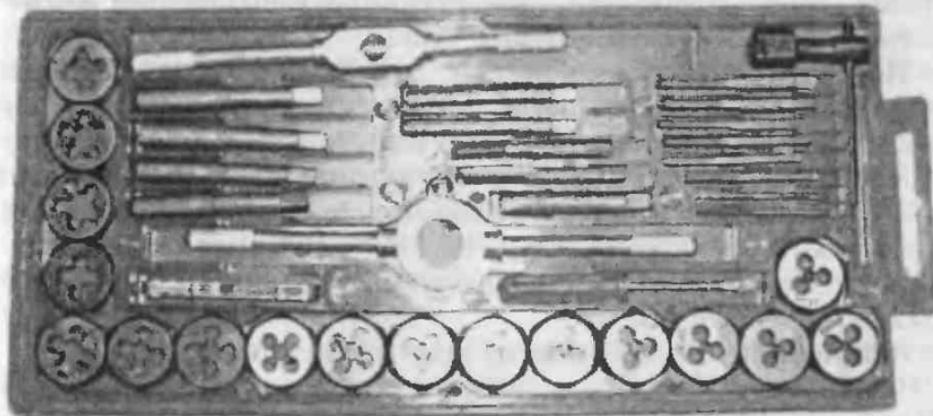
Набор резьбомеров, плашек и метчиков
